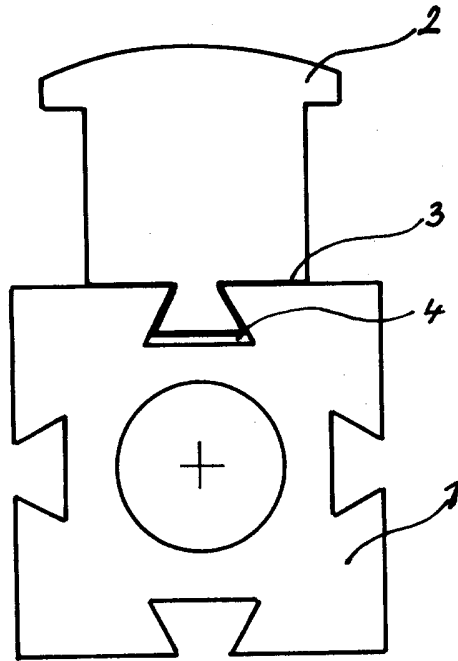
představuje příčný řez rotorem, obr.2 je jako podélný řez.
